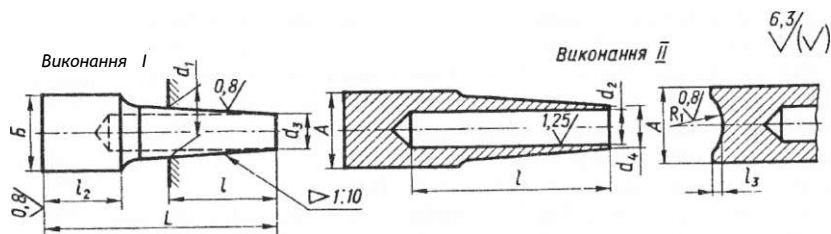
Форма электродів (заготовка) для рельєфного зварювання (розроблені Запорізьким ПКТІ Автопромзварювання. Галузева нормаль ОН 37.0777-74)
